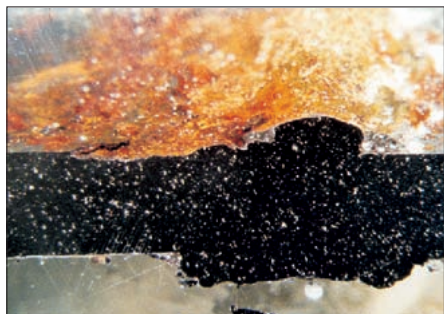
Muldenkorrosion entlang der Schweißnahtkante (Vergrößerung 8x)
